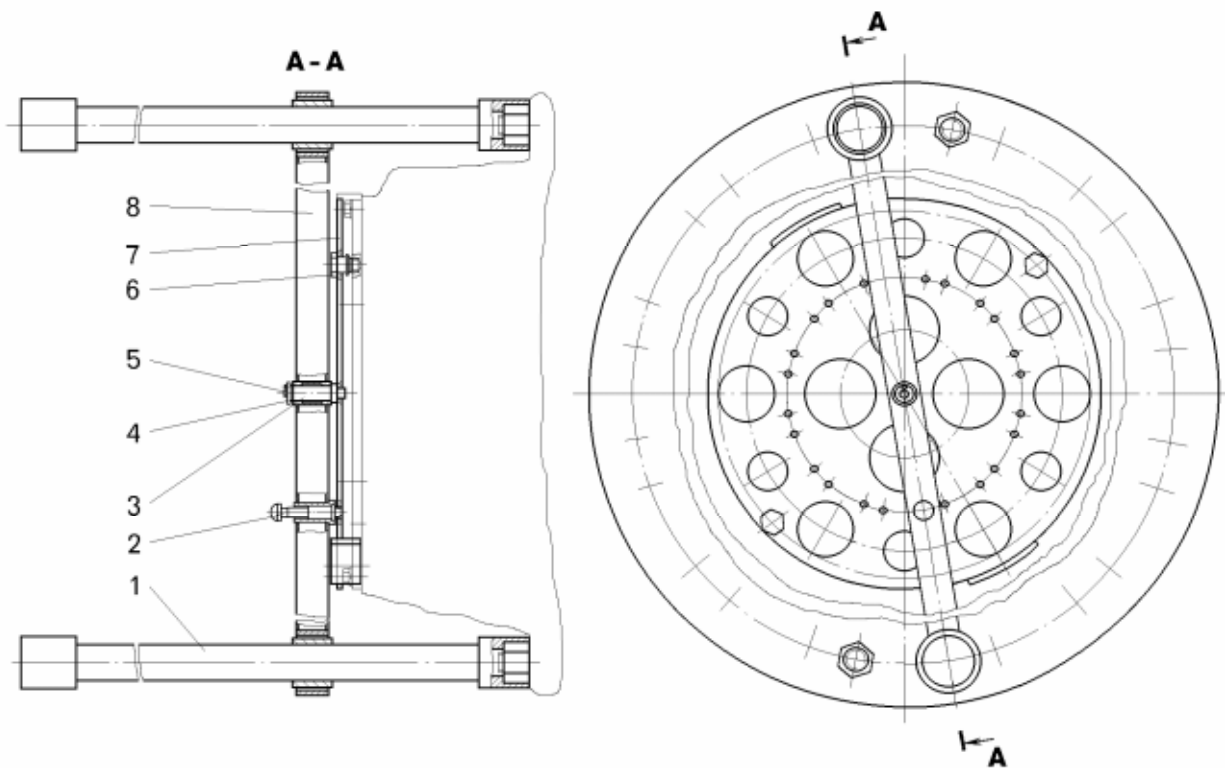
Приспособление для поддержания ключа при отворачивании и заворачивании гаек крепления задних колес:
